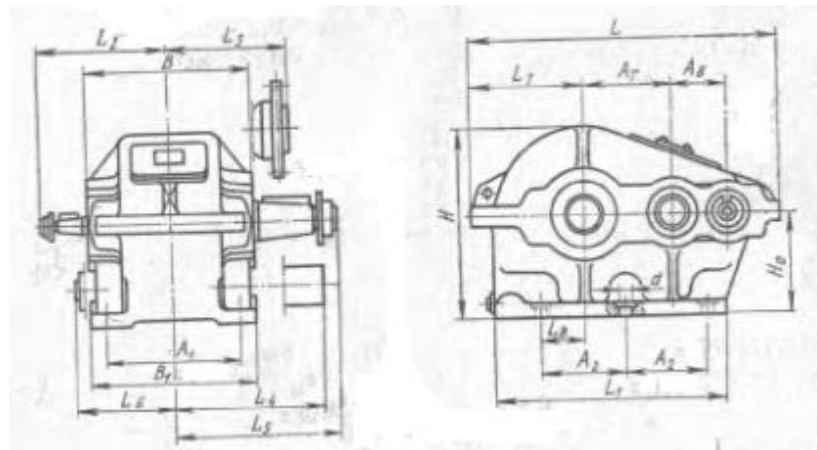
Ескіз редуктора Ц2У-400-К-31,5-22М1
